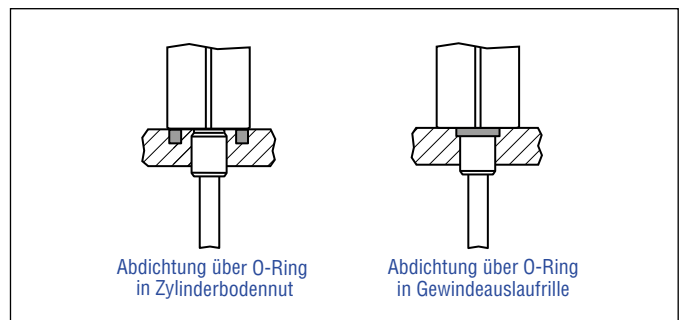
Möglichkeiten der Abdichtung für Gewindeflansch mit flacher Flanschfläche
